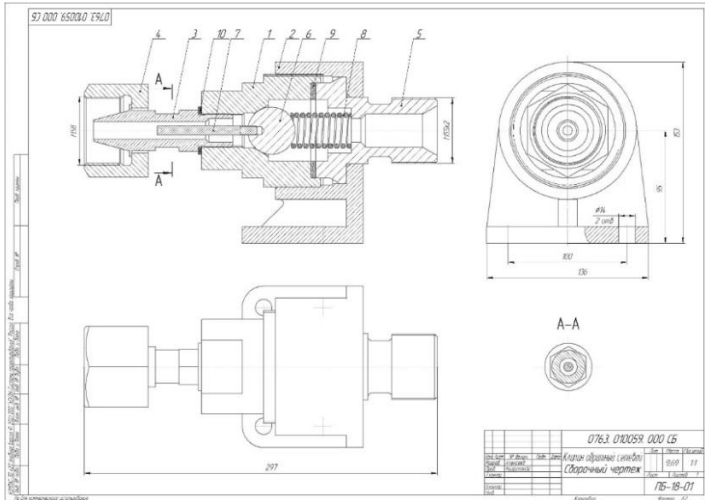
Сборочный чертёж клапана обратного сетевого
